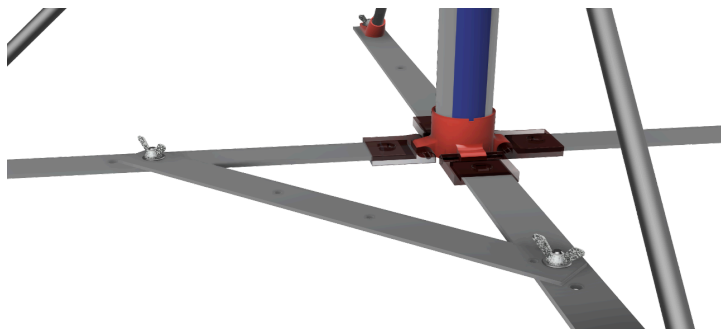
Montaje de la planchuela de soporte de la caja de electrónica
